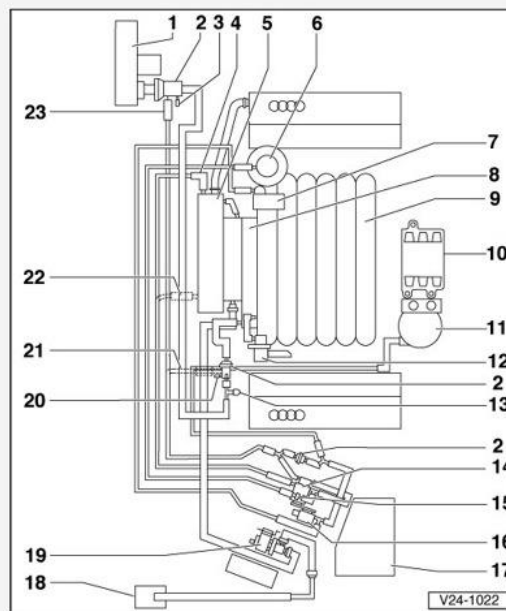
Вакуумная схема двигателя ААН 2.8 AUDI А6 С45
